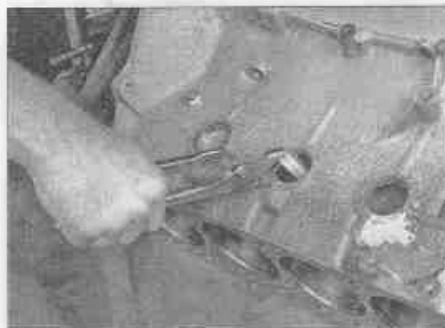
,б. Пассатижами извлеките заглушку из блока
